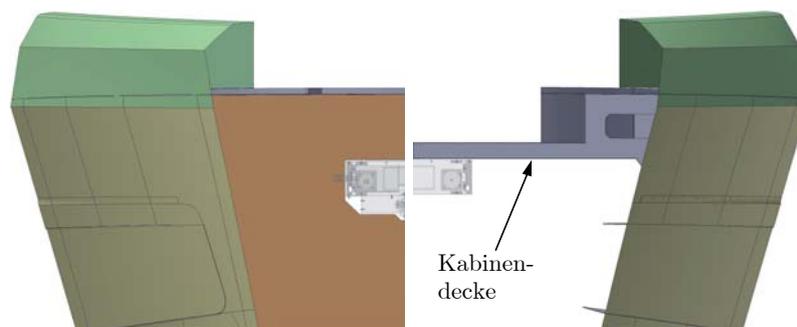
Schottwandausbruch (li.), Einbauhöhe der Ankerlade an der Kabinendecke (r.) (Schnittansichten)
